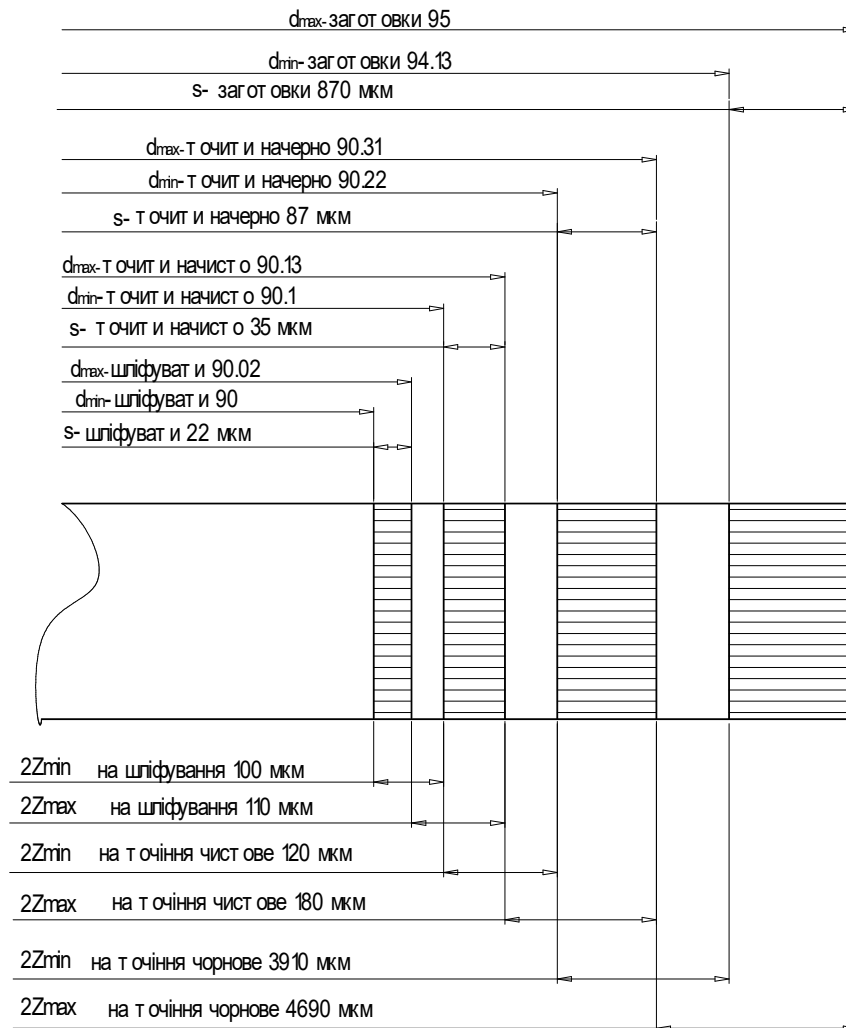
Схема розташування припусків та допусків на обробку поверхні $\varnothing 90h7(^{+0,022})$.
